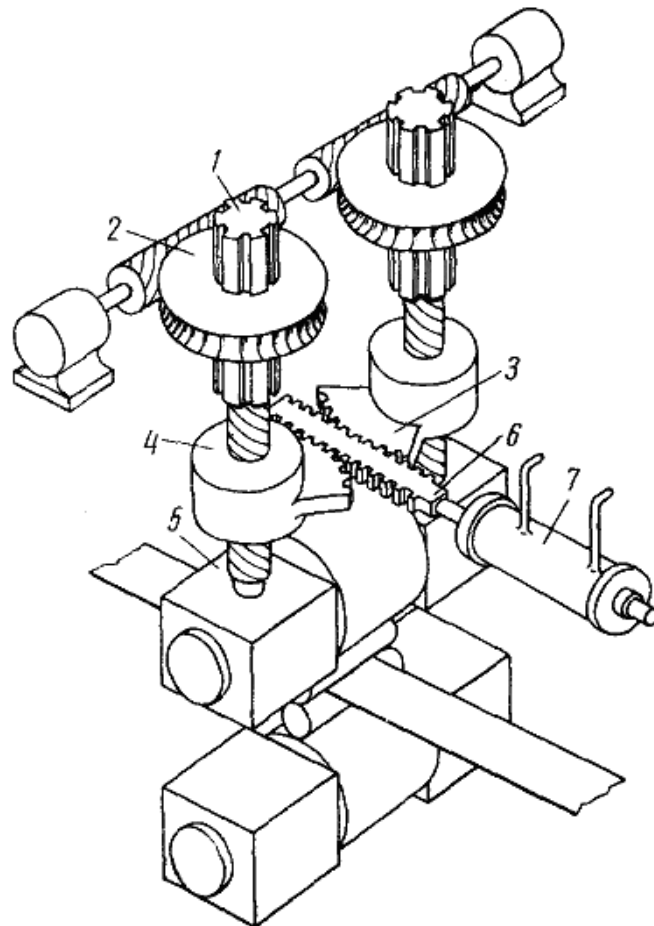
Електрогідрравлічний натискний пристрій: 1 – натискний гвинт; 2 – черв'ячний редуктор; 3 – зубчастий сектор; 4 – гайка натискного гвинта; 5 – подушка опорного валка; 6 – зубчаста рейка; 7 – гідроциліндр
